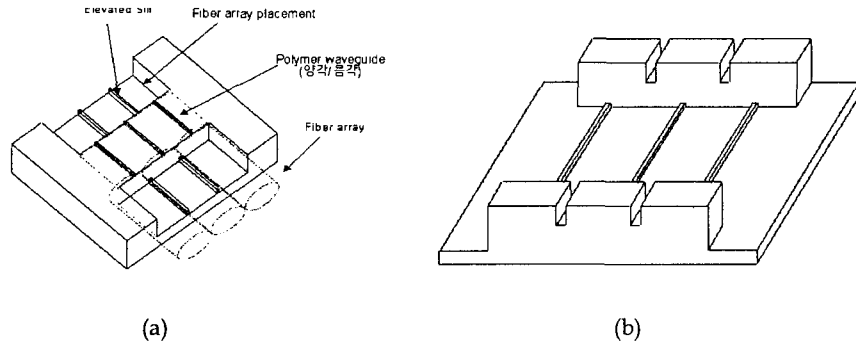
Hot embossing에 요구되는 mold master(a) 및 mold(b).
